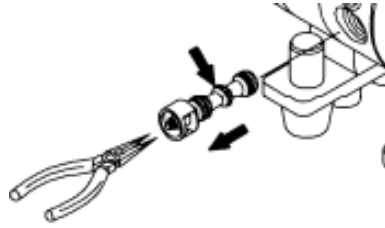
Desmontaje de válvula de carreta y conjunto de manguito 2
